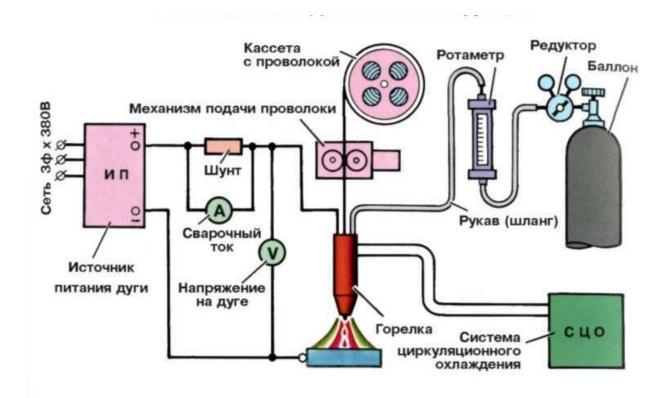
Схема поста для сварки в среде защитных газов.
